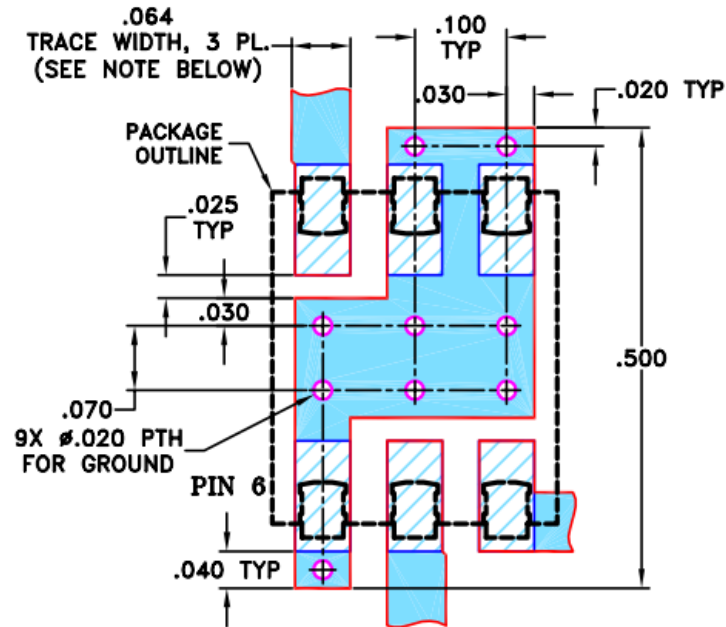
Layout de la PCB suggerida al full d'especificacions [6].
